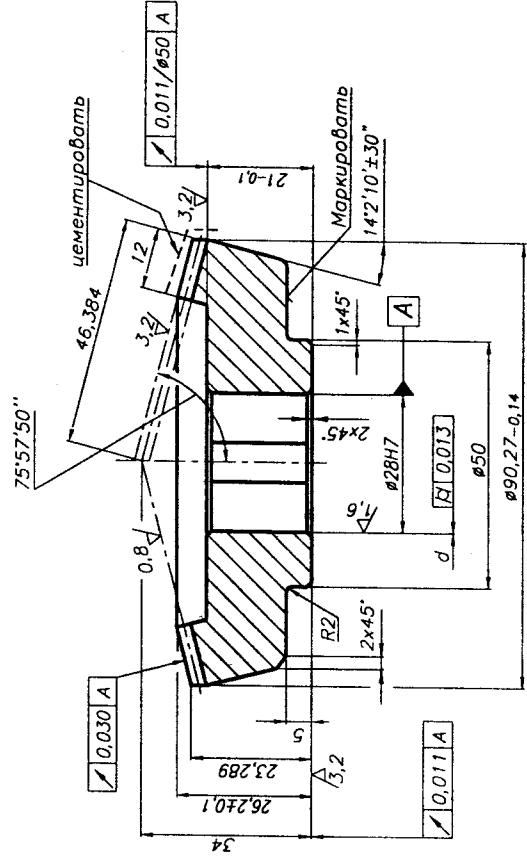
Допуски формы и расположения поверхностей для вариантов 1, 2, 3 выполнения заготовок конического колеса при различных базовых поверхностях для нарезания зубьев
